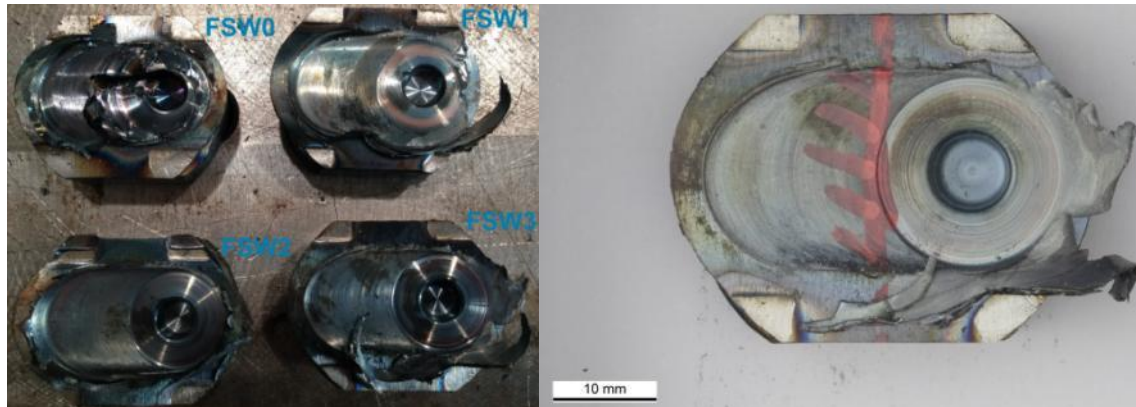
links: Übersicht der rührreibgeschweißten Proben FSW0 bis FSW3; rechts: makroskopische Aufnahme der Draufsicht und Markierung der Schneidelinie, Probe FSW3
